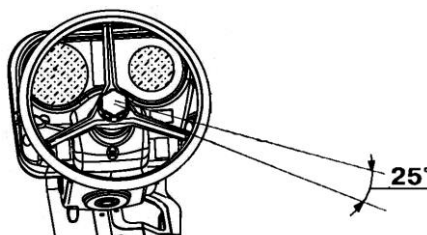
Проверка люфта рулевого колеса.
